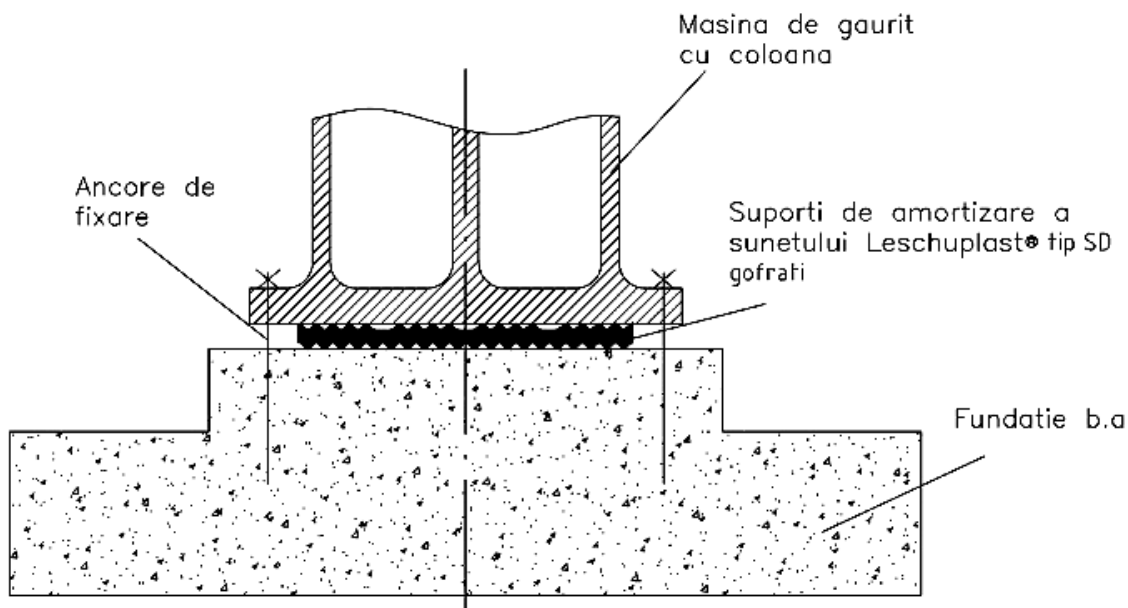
Montarea pe fundație prin suport de amortizare
